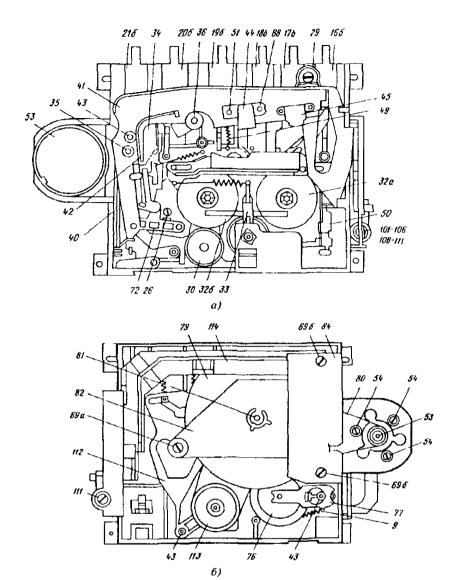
Устройство ЛПМ магнителы «Вега-331»: *а* — вид спереди (кассетоприеминск и крышка святы):
